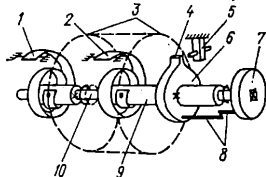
Кинематическая схема извещателя МДПИ-028.
